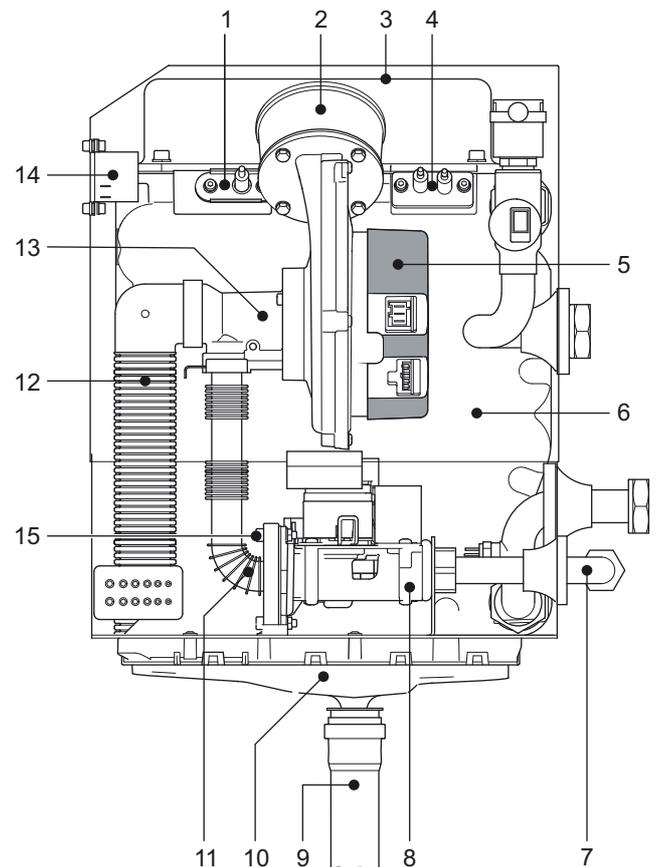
Gasbrenner der GCU compact - Explosionsdarstellung
